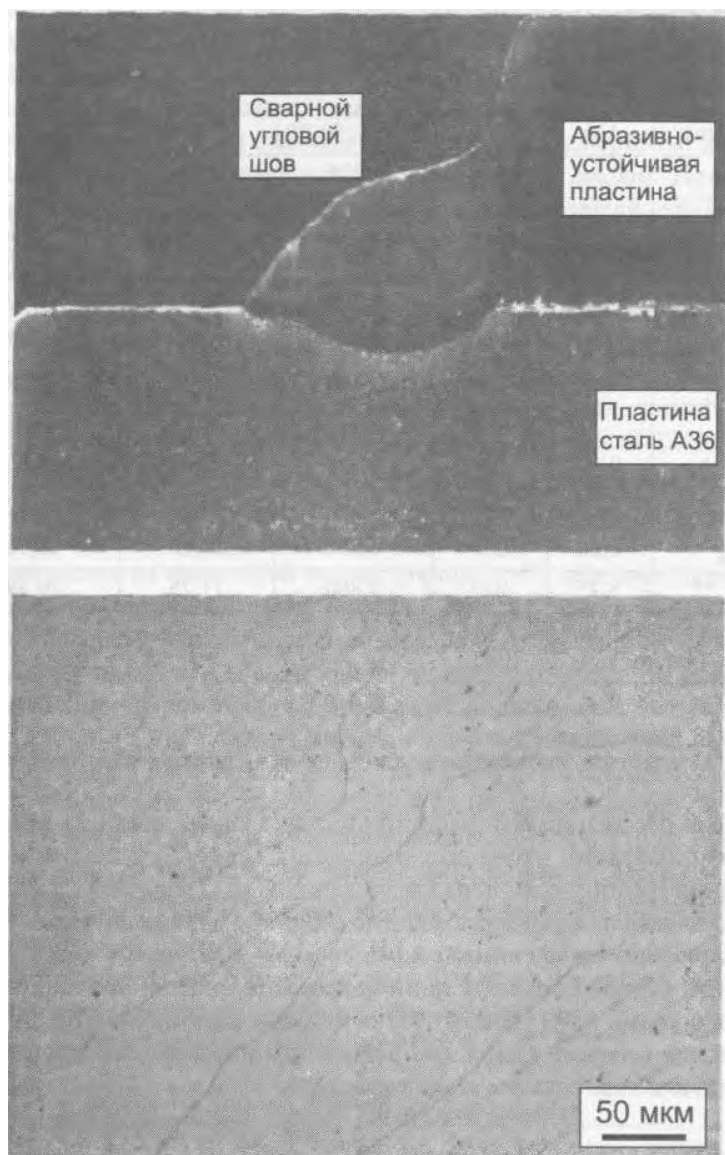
Угловой однопроходный шов сварного соединения конструкционной стали марки А36 с абразивно-устойчивой сталью с использованием присадочного металла 18 8 Мп [20]
